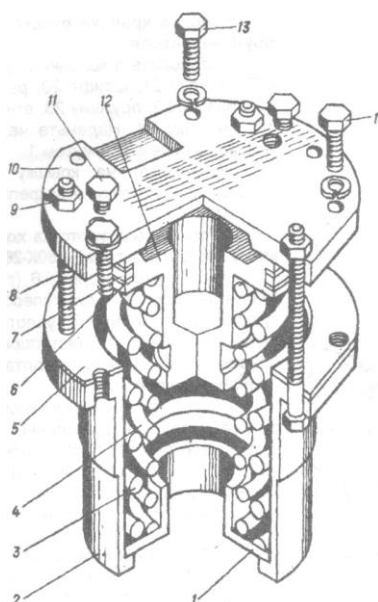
Складання гідроакумулятора: 1 — днище; 2 — корпус; 3, 4 — пружина, 7— прокладка; 6 — шайба; 7 — кільце ; 13 — болт; 9 — гайка; 10 — кришка, 1 — пробка; 12 — поршень.
